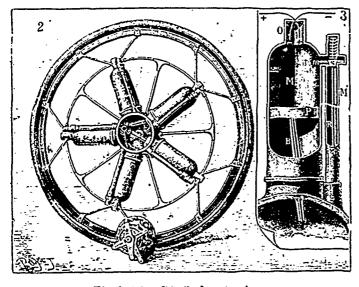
et S.—Déteils du mécanisme. Fig. 2. Vue du moteur, la boîte-moyen étant enlerce. - Fig. 3. Coupe d'un cylindre.
